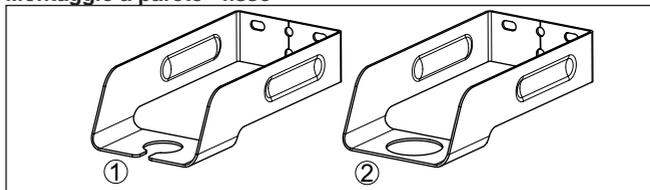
Staffa di montaggio per montaggio a parete - fisso
